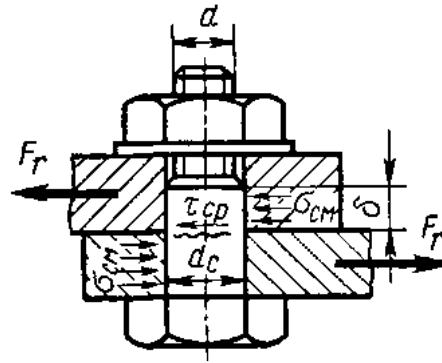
К расчету соединения, нагруженного поперечной силой при установке болта без зазора
